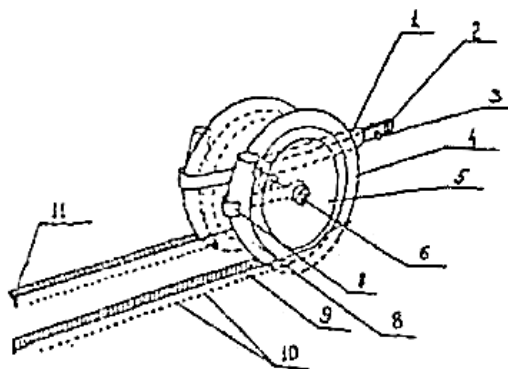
Технологический процесс работы двухдискового сошника с внешними ребрами-бороздкообразователями-уплотнителями: 1 – корпус; 2 – отверстие; 3 – болт; 4 – диск; 5 – ребра-бороздкообразователь-уплотнитель; 6 – ось; 7 – пластина; 8 – семянаправитель; 9 – бороздка; 10 – семена; 11 – щель
